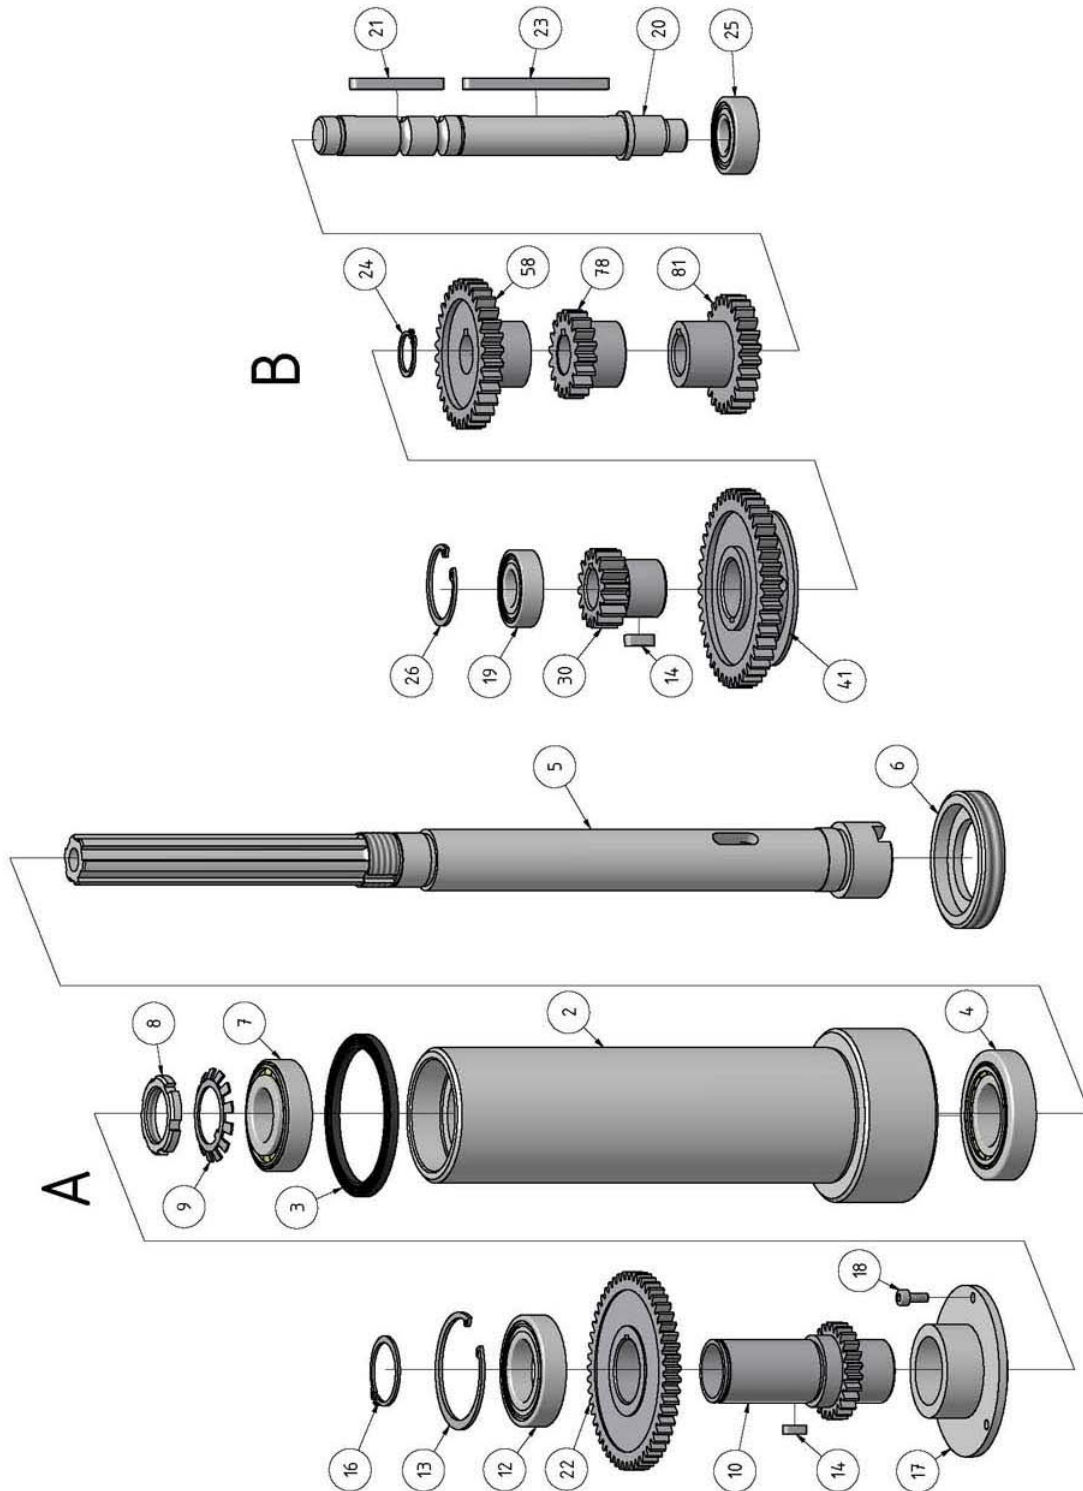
Fräskopf 2 von 6 - Cabezal fresador 2 de 6
